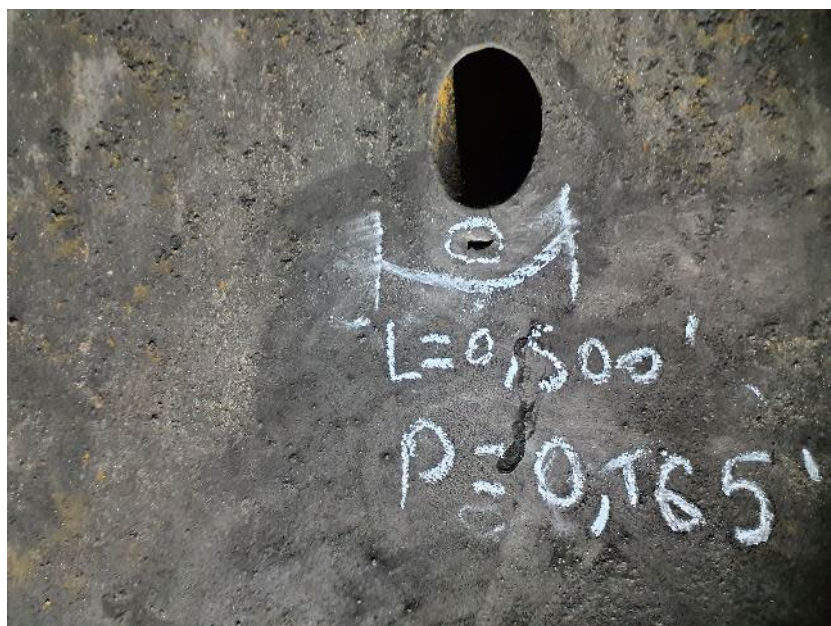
Falta de fusión en soldadura interna de acometida de 2"
